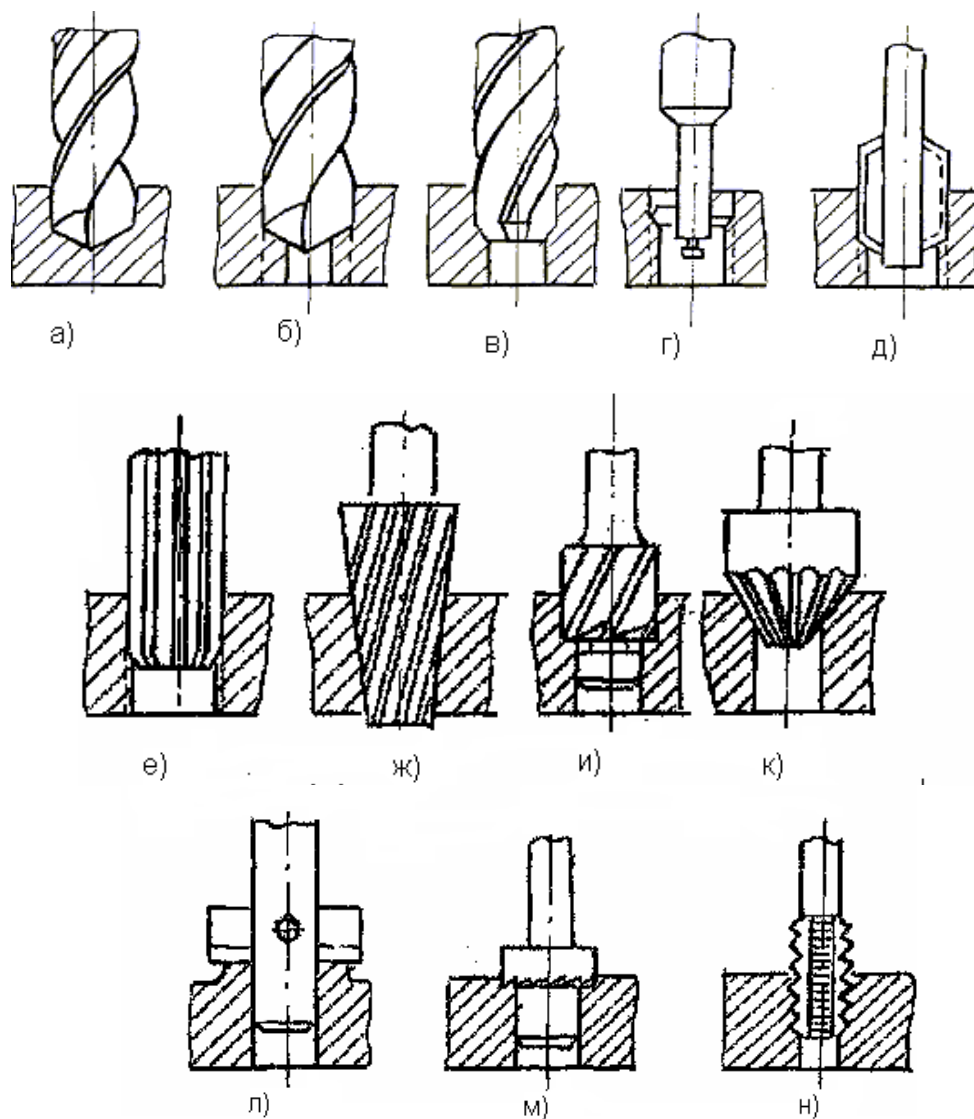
Схеми одержання і обробки отворів на свердильних верстатах
